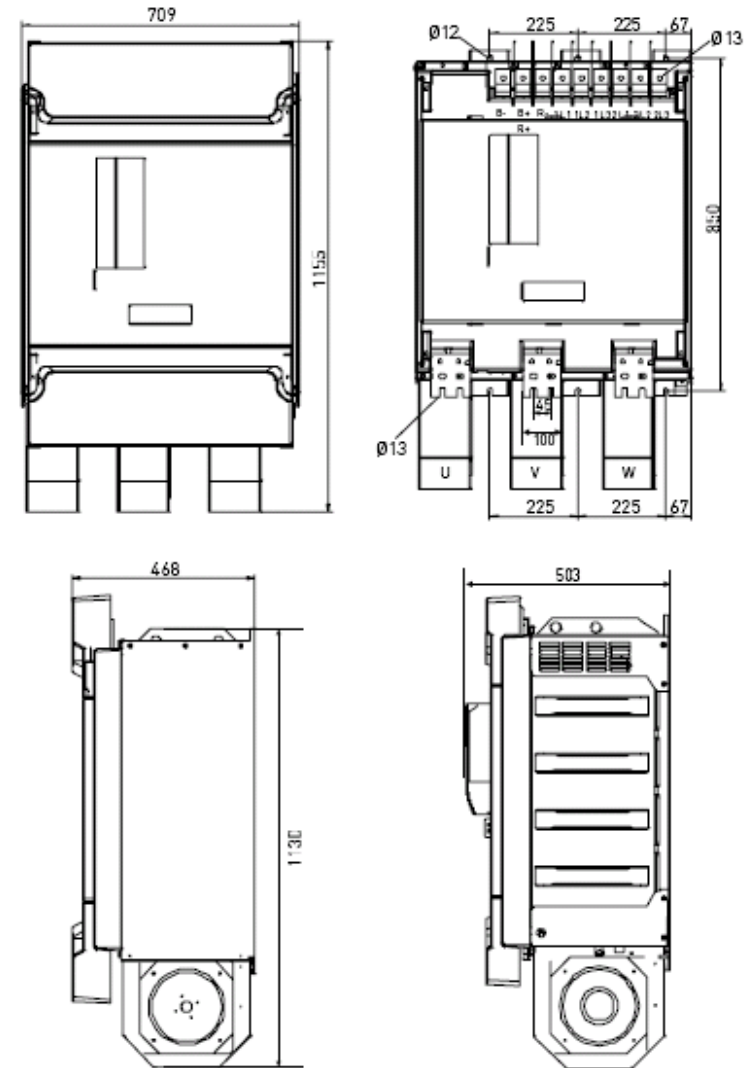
Габариты типоразмера FR11(вес = 210 кг)
